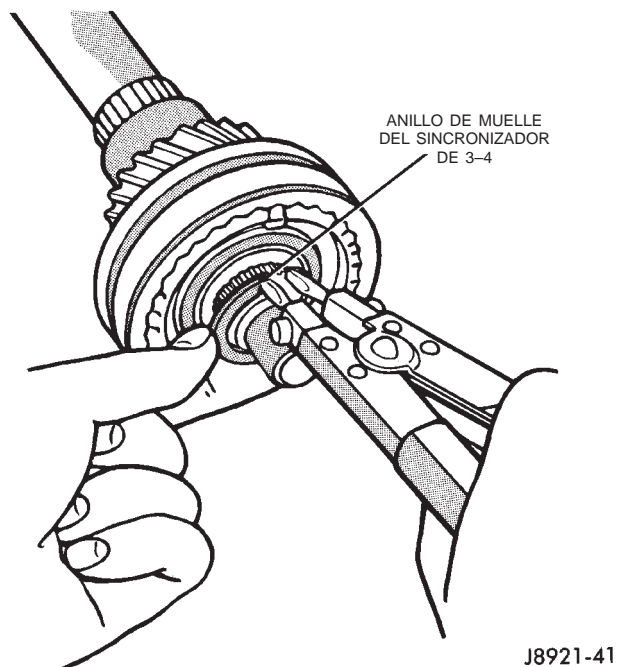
Desmontaje del anillo de muelle del sincronizador 3-4
